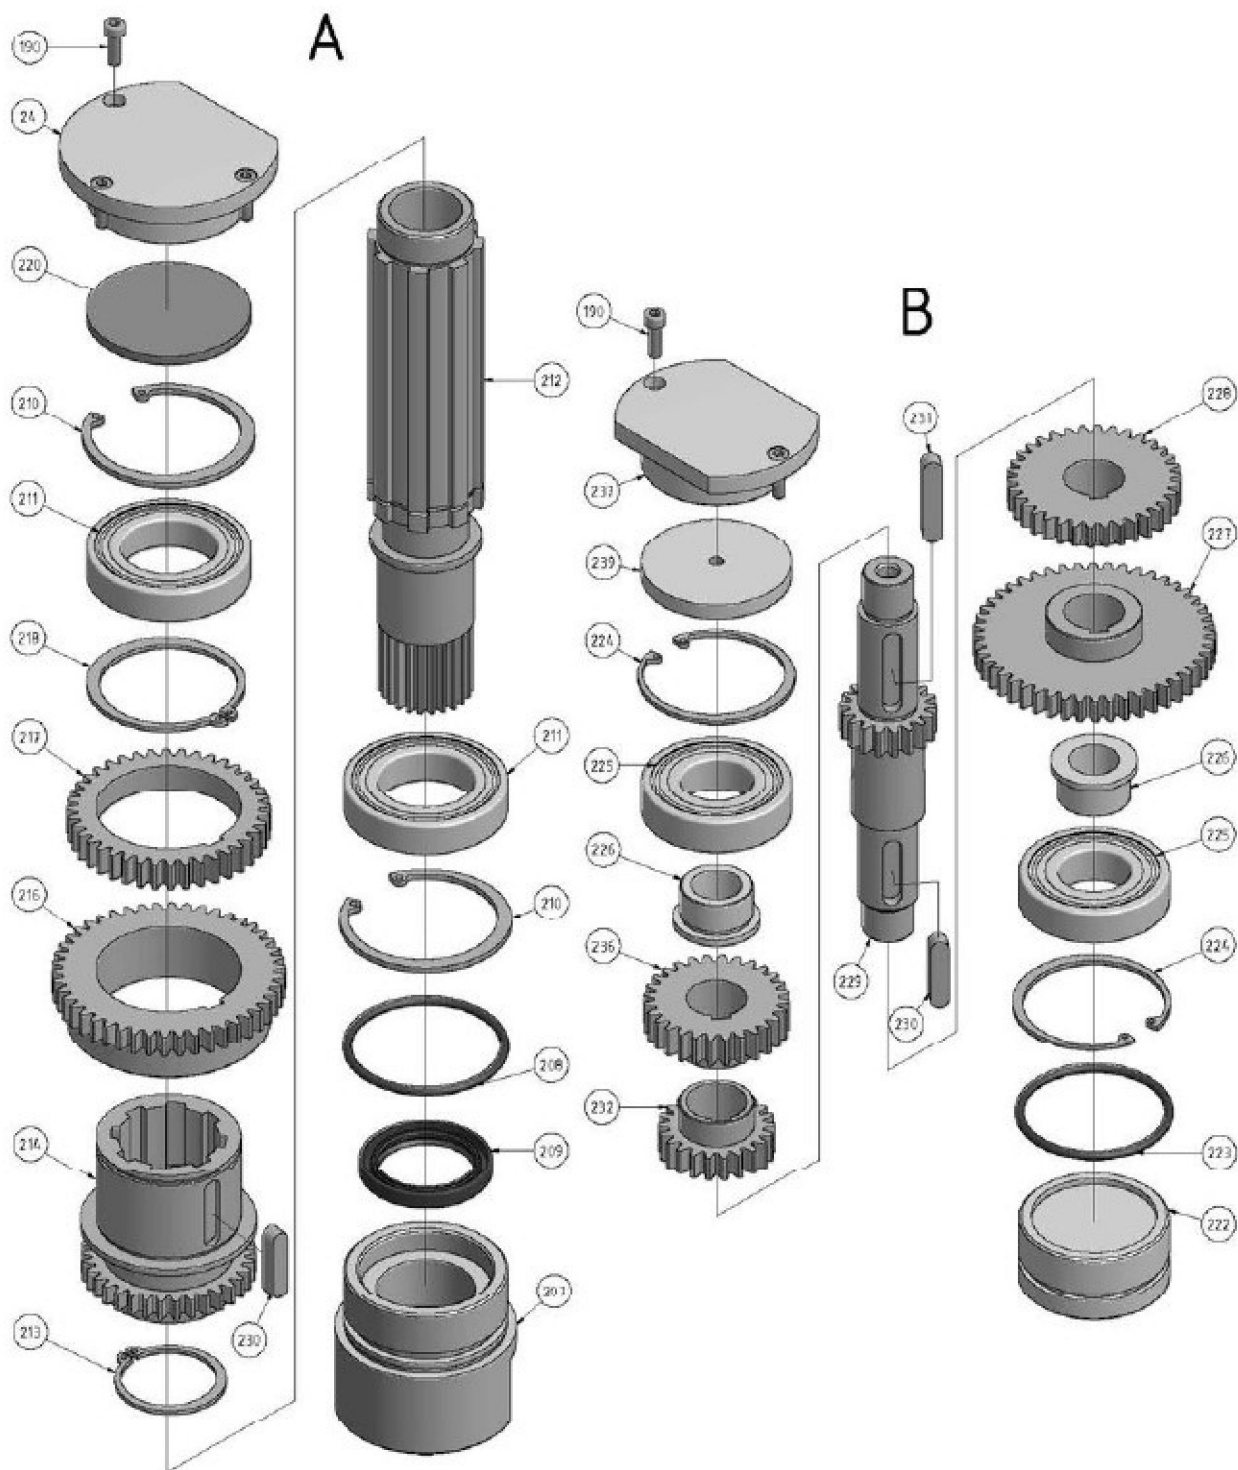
husillo principal caja de engranajes 1 de 4 - Gear box main spindle 1 of 4
